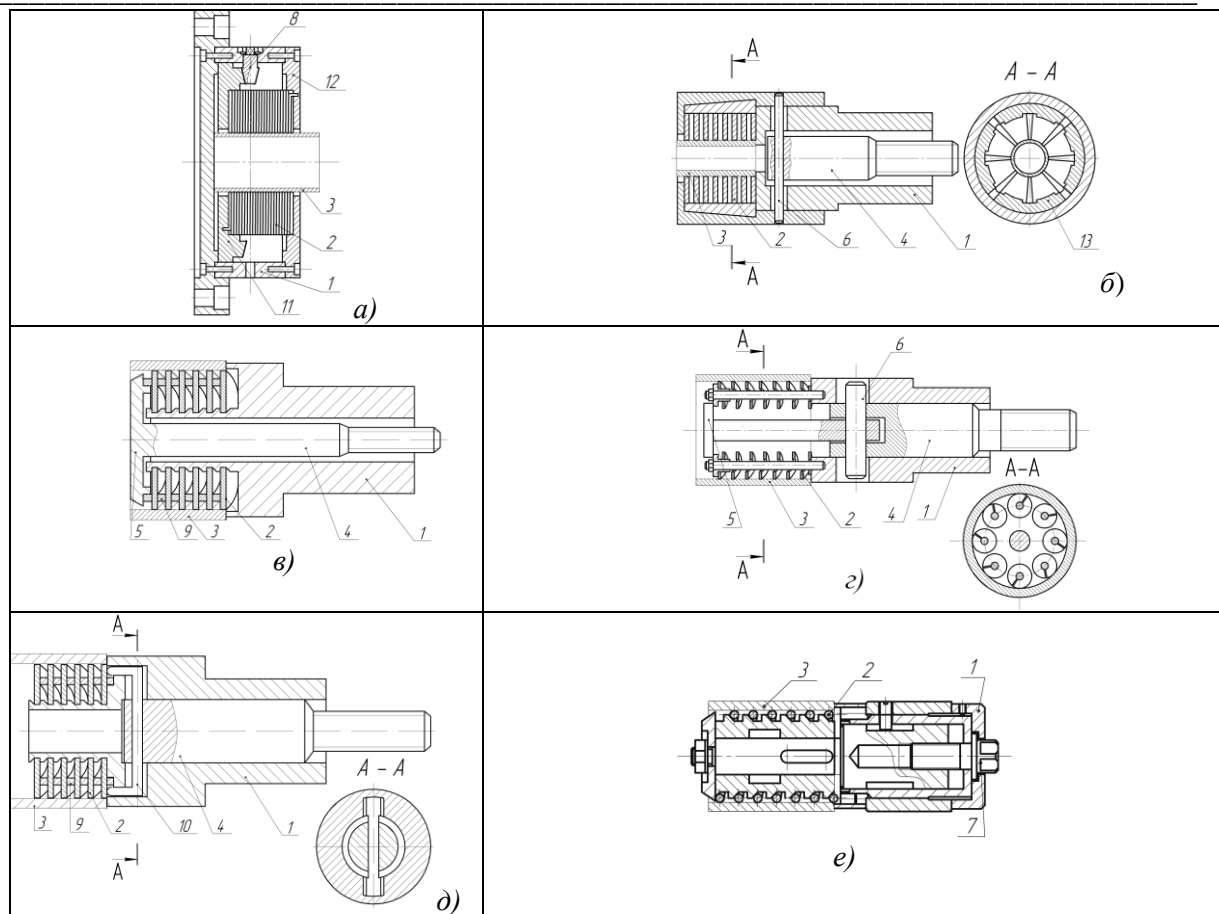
Синтезовані конструкції патронів для запуску тонкостінних втулок, захищених Пат. України: а – №16500; б – № 19342; в – № 15685; г – № 17465; д – № 16499; е – № 20308: 1 – корпус; 2 – гвинтовий запискний елемент; 3 – заготовка; 4 – тяга; 5 – упорна головка; 6 – палець; 7 – регулювальна гайка; 8 – конічна шестерня; 9 – упорна спіраль; 10 – П-подібний віджимник; 11 – центральне зубчасте колесо; 12 – кришка; 13 – кулачки направляючі; 14 – підшипник.
